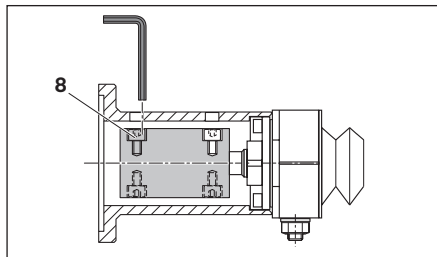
Motorseitige Befestigungsschrauben der Kupplung
